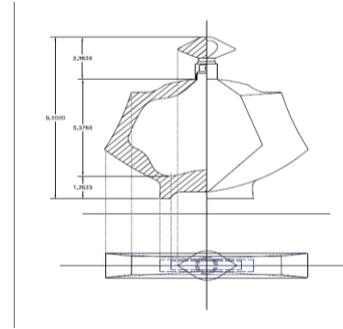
مسقط رأسي وأفقي وقطاع للفكرة التصميمية الرابعة
